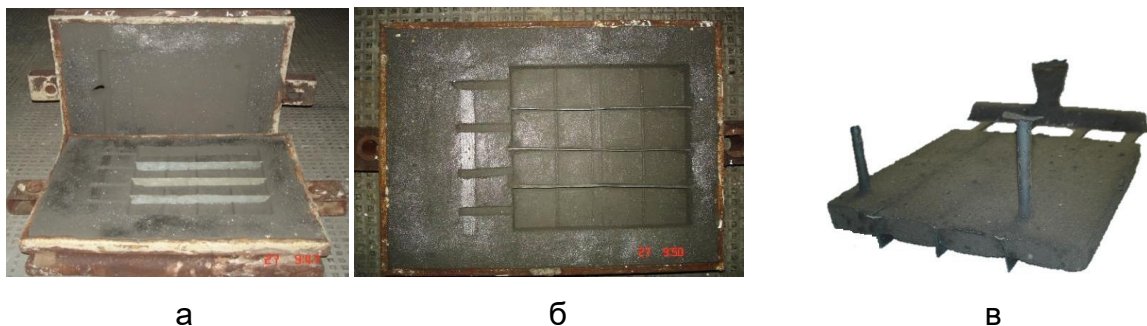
Ливарна форма з розміщеними в порожнині сталевими пластинами (а, б) і загальний вид отриманого виливка «Горизонтальна плита» (в)
